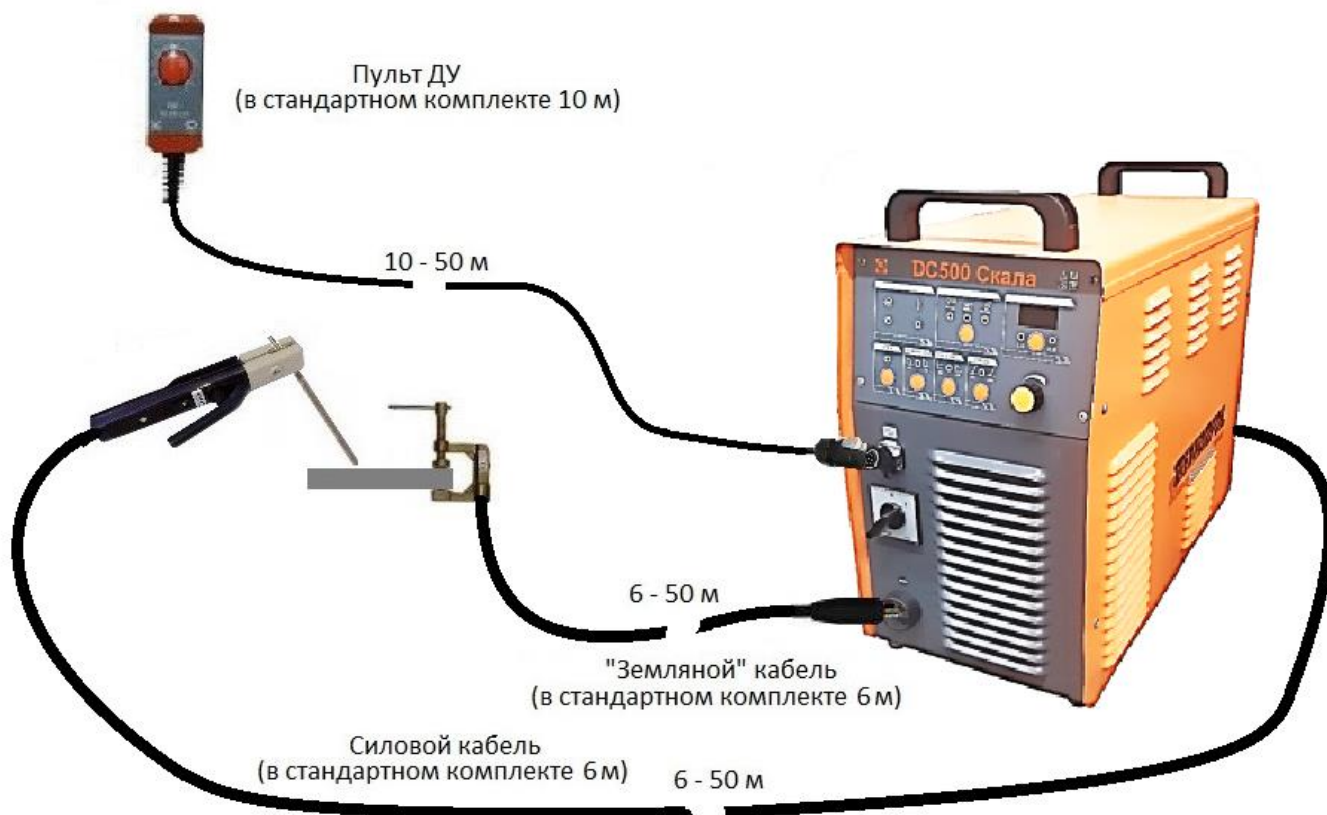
Схема подключения источника в режиме сварки РД
